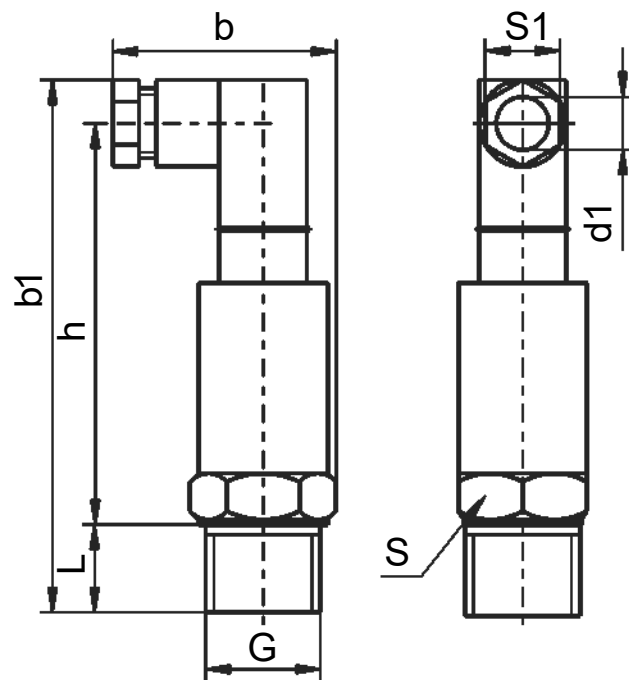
Габаритные и присоединительные размеры датчиков давления измерительных РПД-И, РПД-В и РПД-ИВ.
